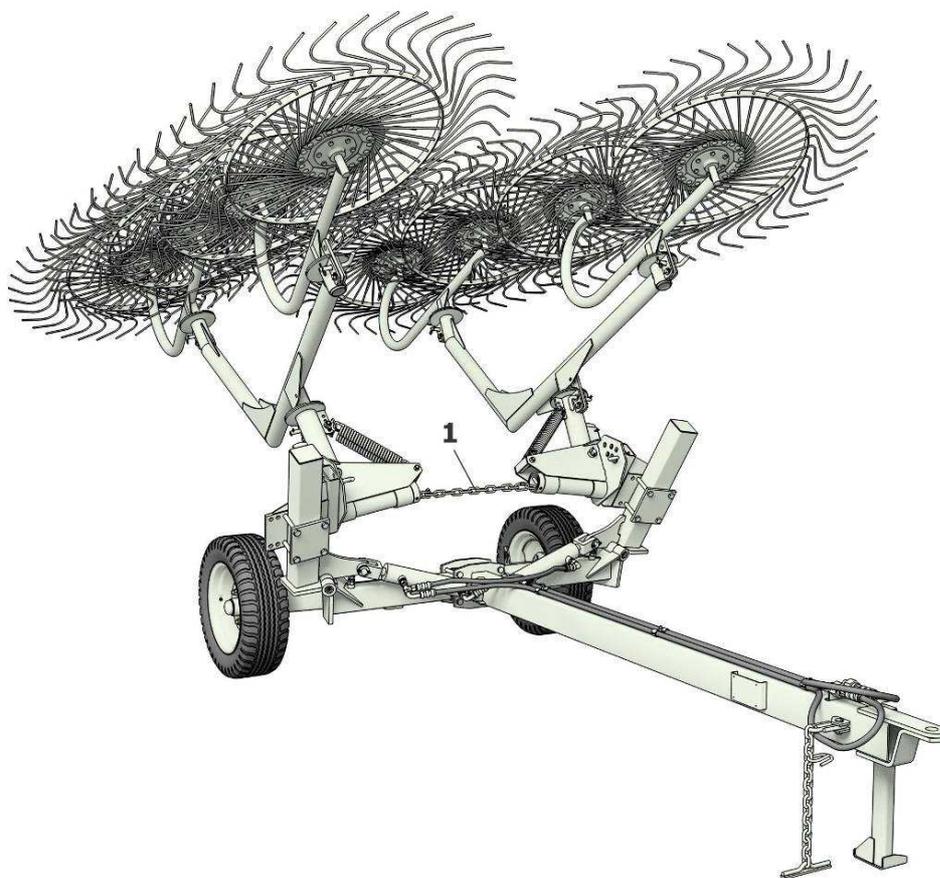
Схема установки секций рабочих колес при оборачивании валка
